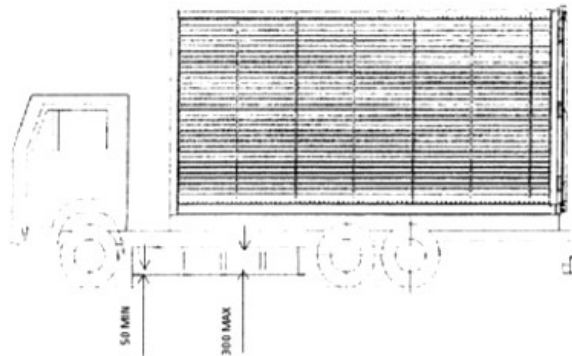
, Dimensiones de los largueros, Vista Lateral (dimensiones en mm)
